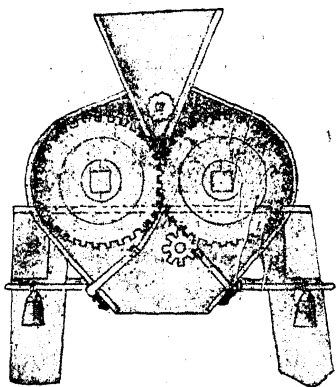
Плющильные цилиндры для раздавливанія сѣмянъ въ мязгу. Сверху воронка, внутри ея зубчатое колесо. Внизу справа и слѣва двѣ скребки съ рычагами и противовѣсами. Нижнею зубчаткою приводится въ движеніе одинъ изъ валовъ и шкивомъ валикъ въ воронкѣ.
